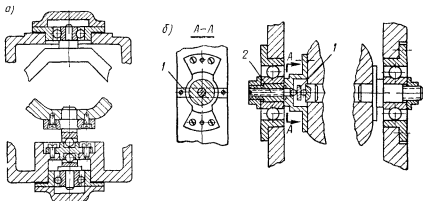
Схема крепления подшипников с гладкой внутренней поверхностью наружного кольца
